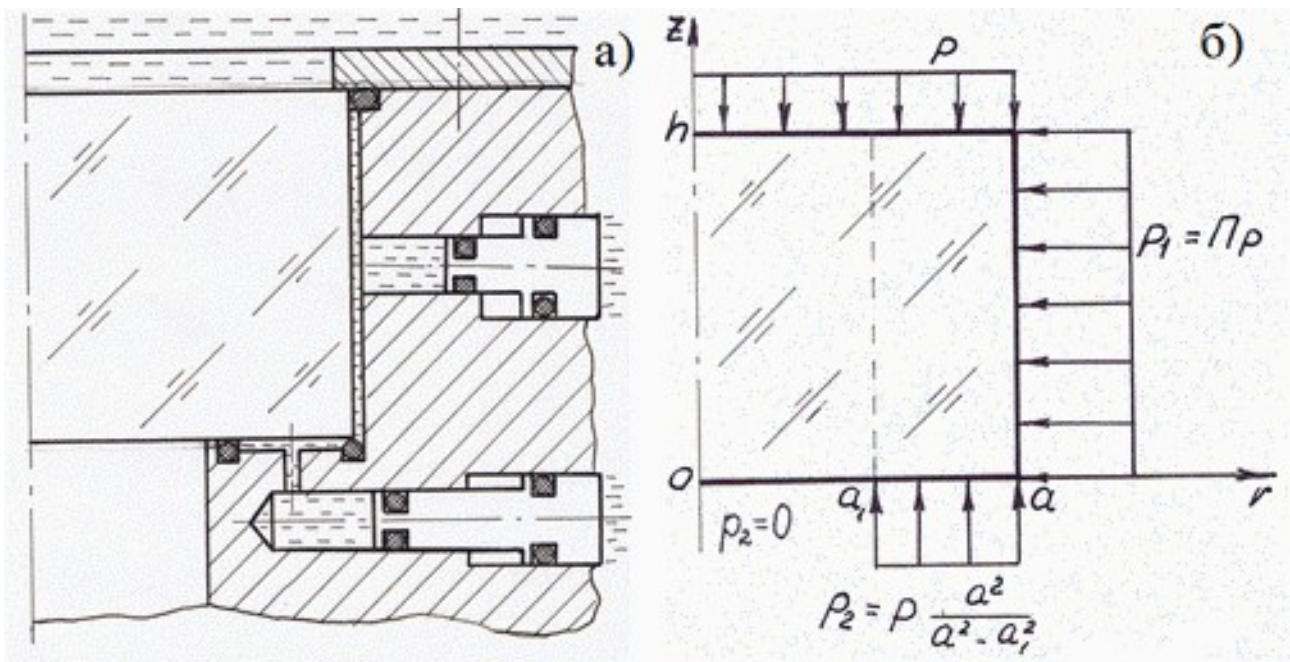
Рассматриваемая конструкция (а) иллюминатора для высоких давлений и схема нагружения (б) его светопрозрачного элемента.
